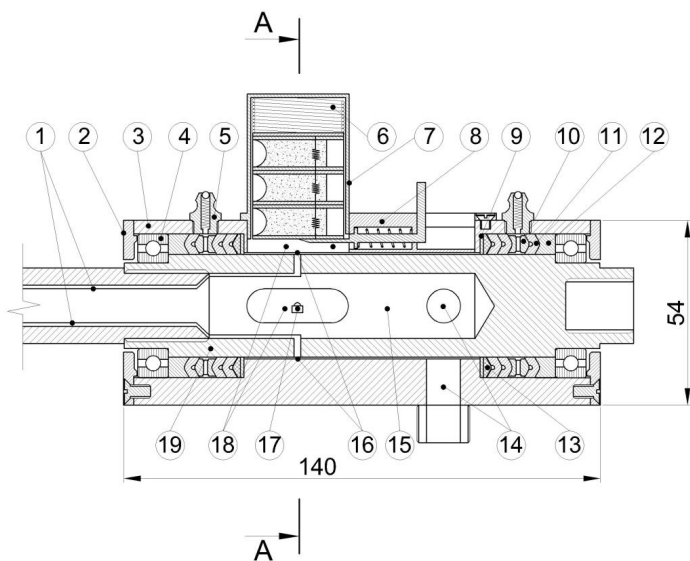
Вертлюга модифікований для реалізації вибухо-механічного руйнування: 1 – струмопровідні дроти (220 В); 2 – кришка вертлюга; 3 – корпус вертлюга; 4 – підшипник 25x42x9 мм (ГОСТ 8338-75); 5 – прес-маслянка 1.1 Ц6 (ГОСТ 19853-74); 6 – пружина подавача зарядів вибухової речовини; 7 - касета з зарядами вибухової речовини; 8 – затвор; 9 – кільце металеве; 10 – кільце для
